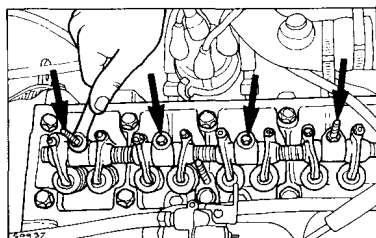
Болты и гайки крепления оси коромысел (указаны стрелками)
